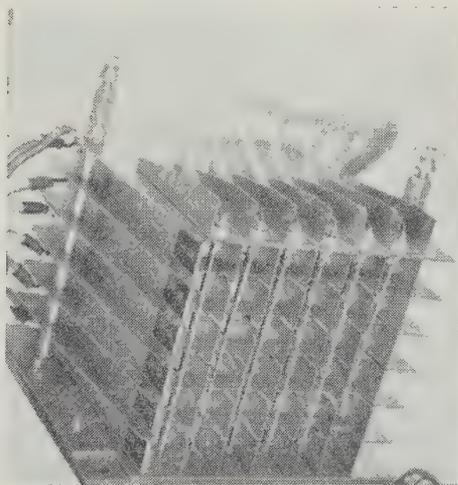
Mélangeur du multiplex alvéoles assemblés.
